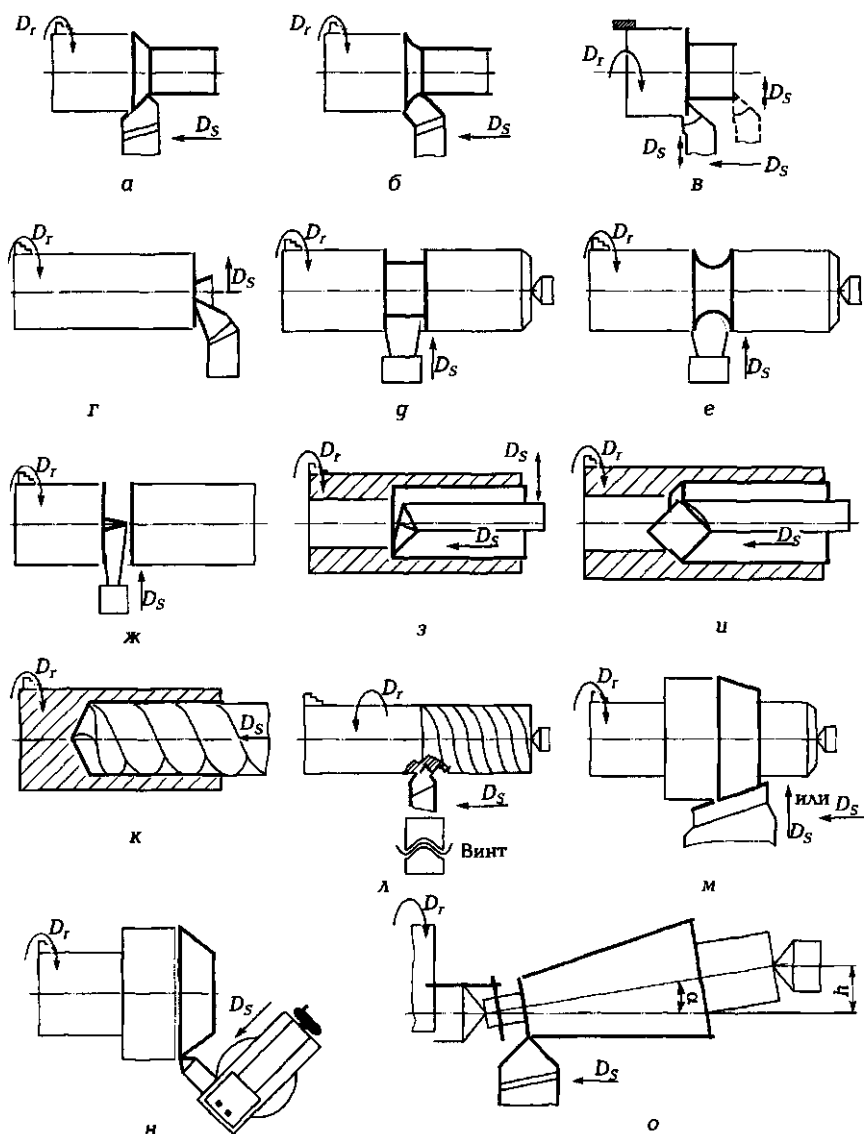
Основные схемы обработки заготовок на универсальном токарно-винторезном станке:
